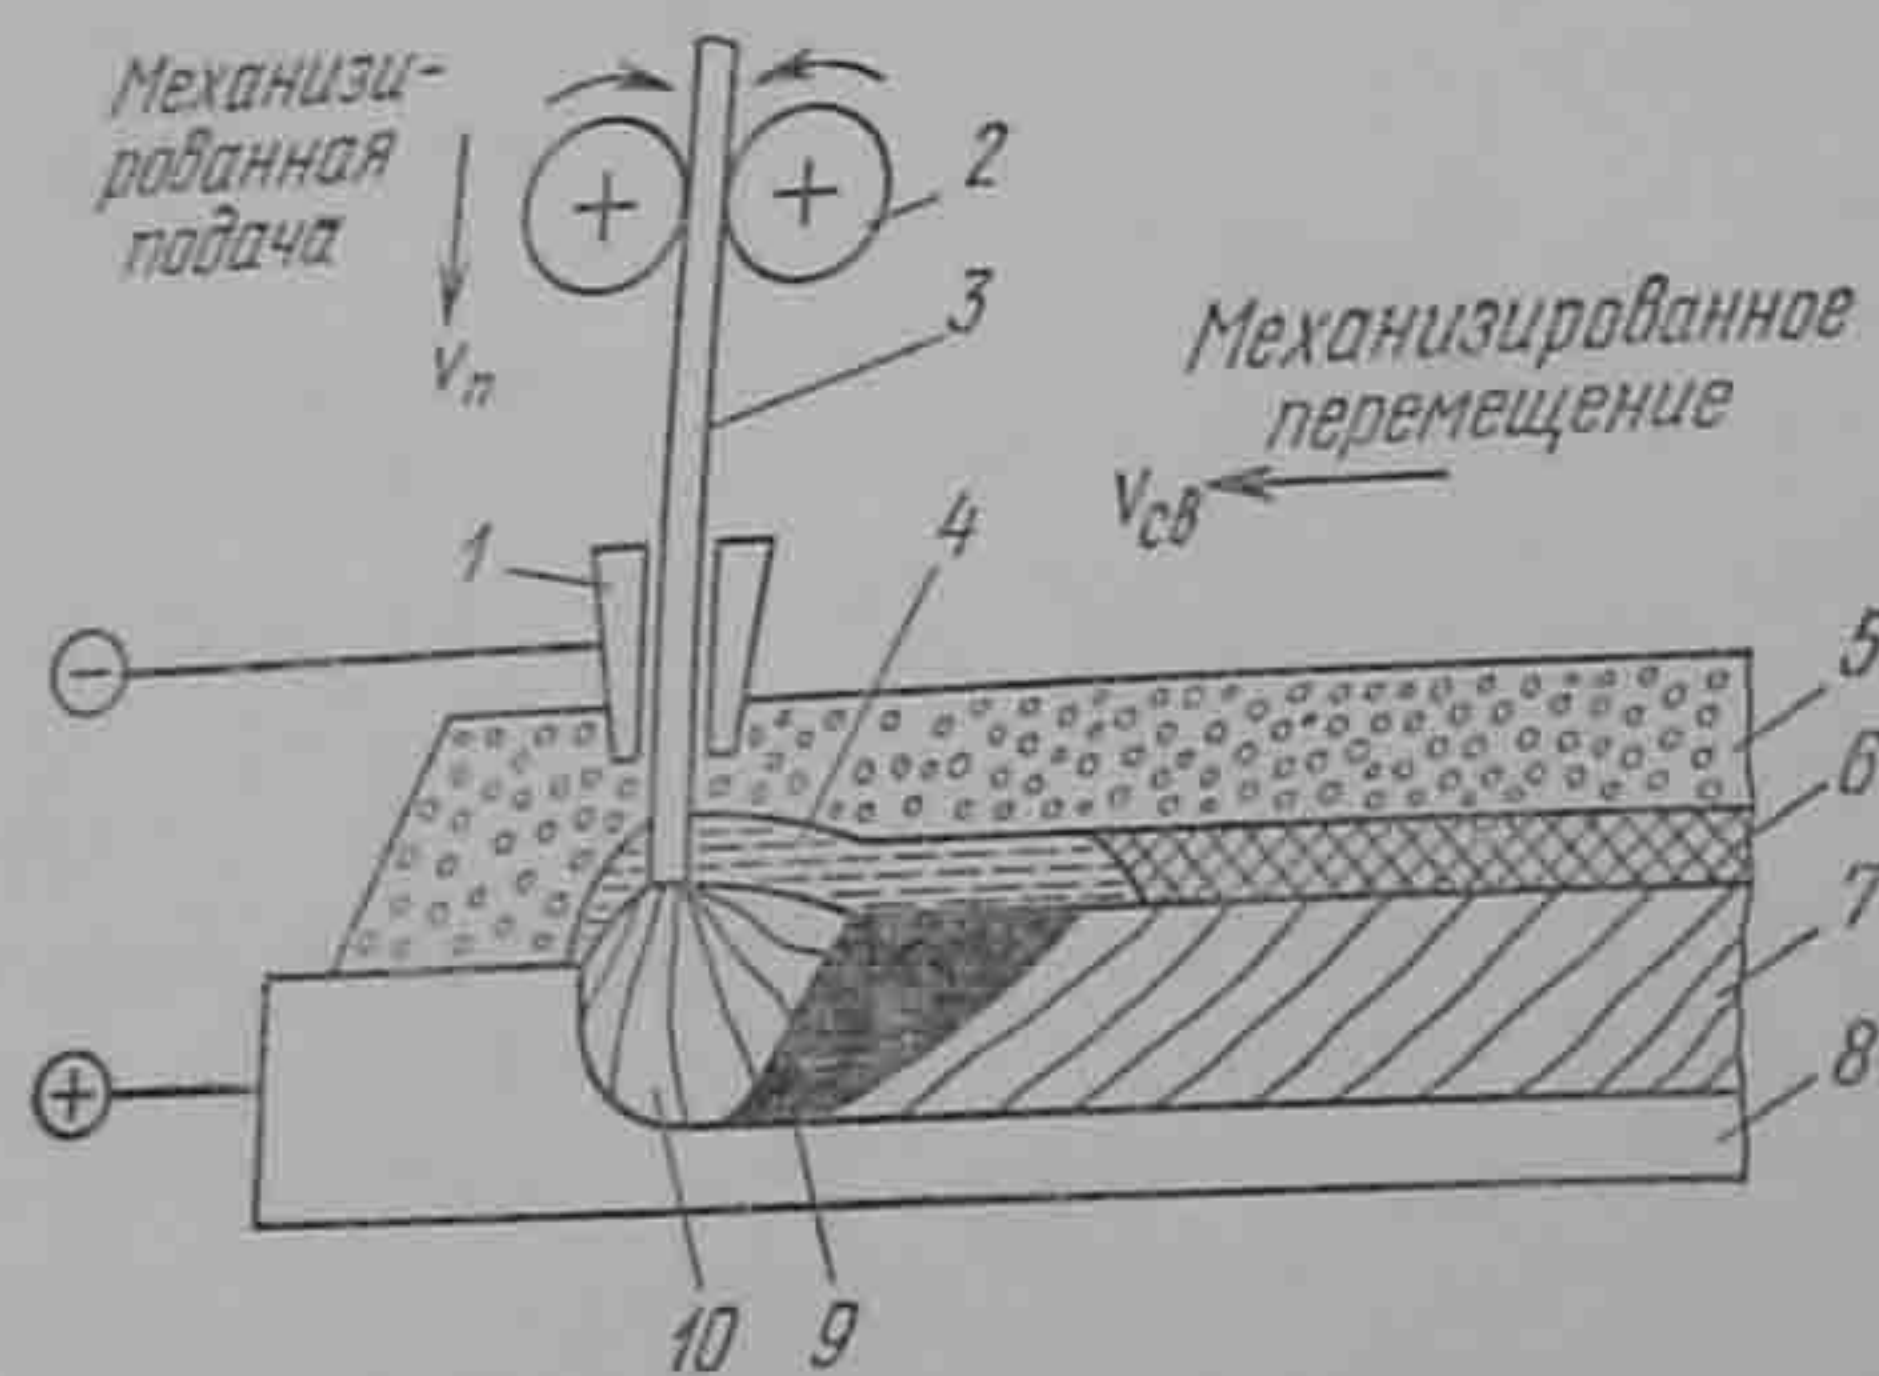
Схема автоматической дуговой сварки под флюсом
